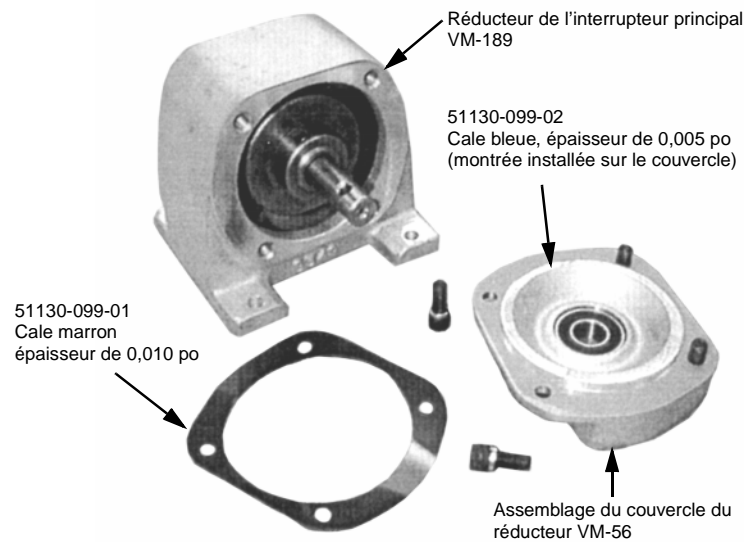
Installation des cales sur l'assemblage du réducteur de l'interrupteur principal VM
